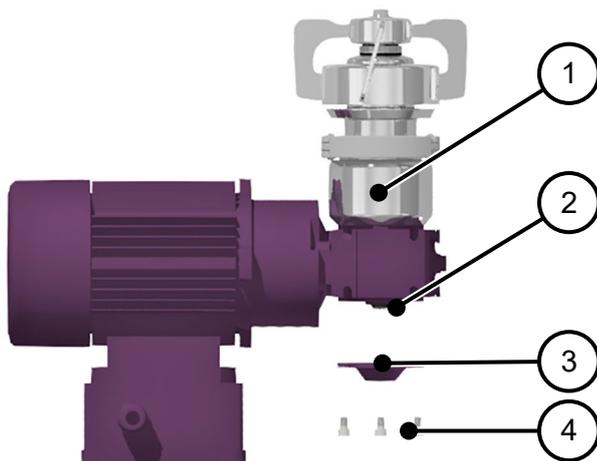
Maschine mit Abdeckhaube (Explosionsdarstellung)
